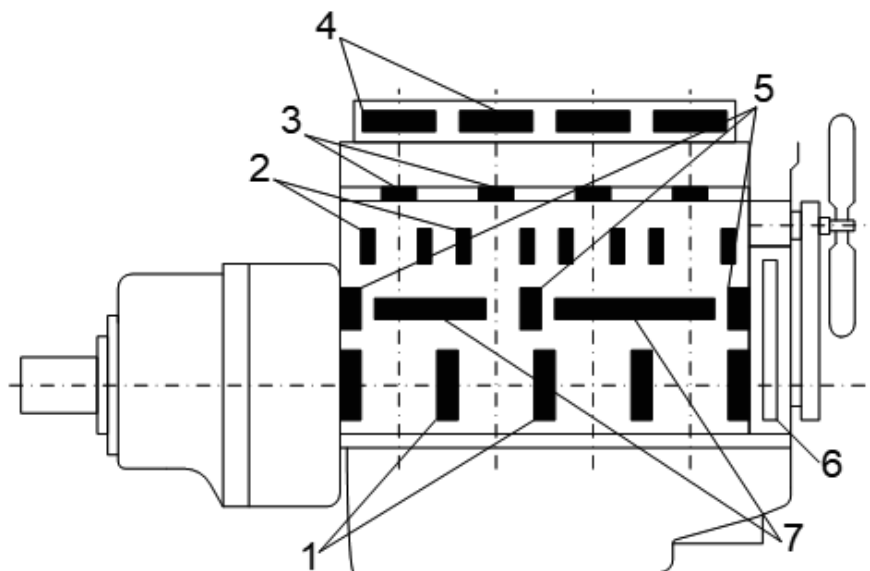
Місця розташування сенсорів на корпусі двигуна:
